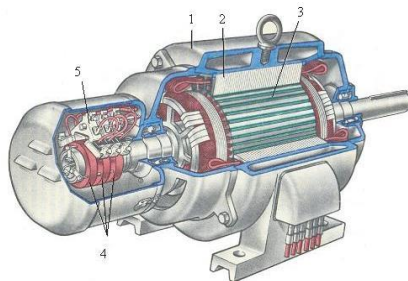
Асинхронный двигатель с фазным ротором в разрезе: 1 – станина; 2 – обмотка статора; 3 – ротор; 4 – контактные кольца; 5 – щетки
